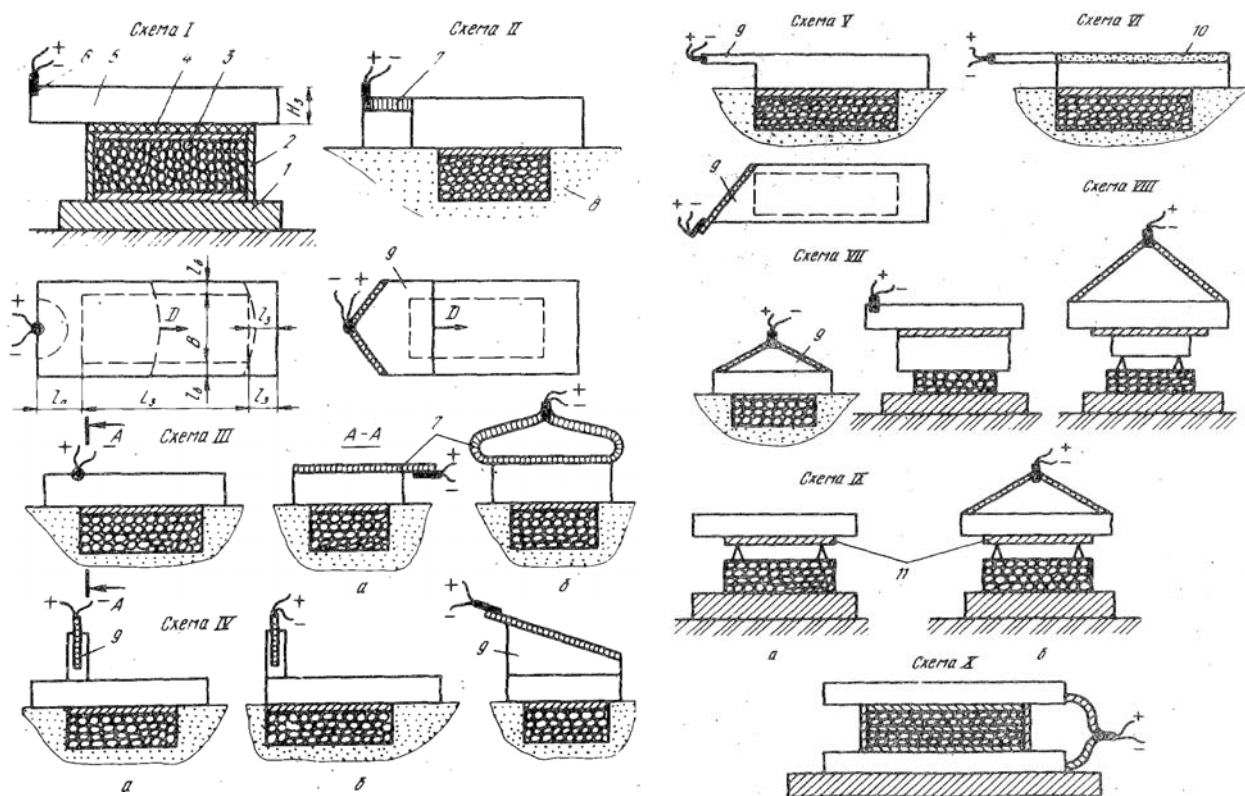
Схемы взрывного прессования плоских заготовок:
